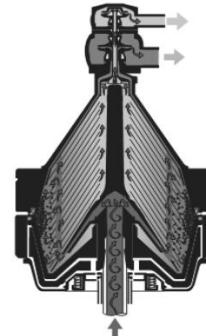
Барабан двухфазной установки Vactofuge с непрерывной выгрузкой бактофугата
